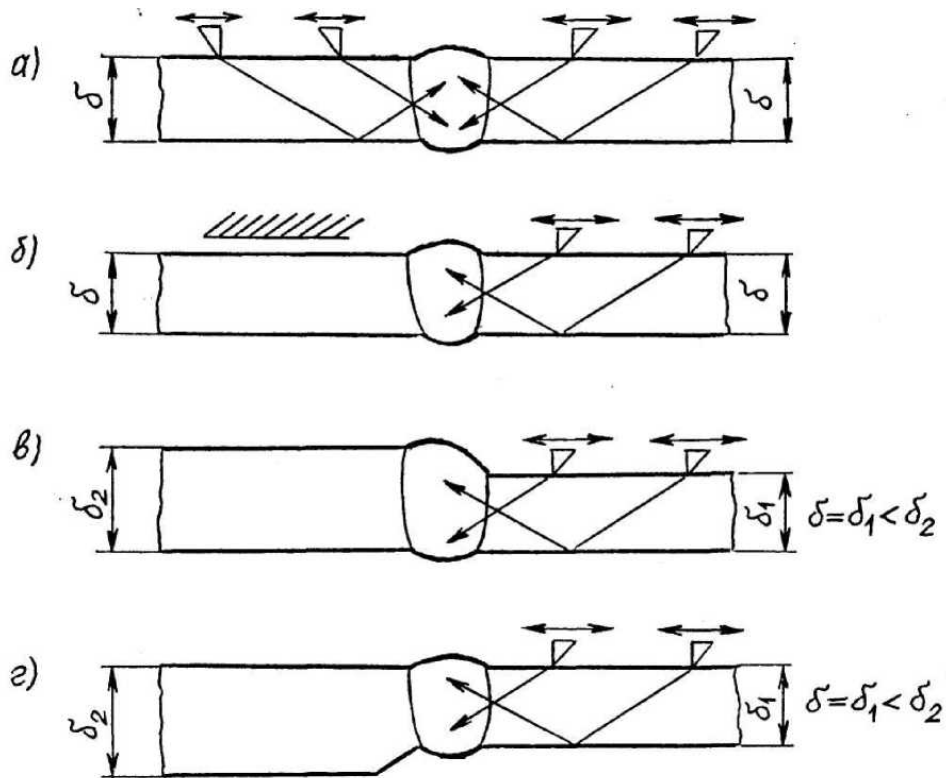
Схема проведення ультразвукового контролю: а) – з двох сторін зварного шва в одній площині; б) – з однієї сторони зварного шва; в), г) – різнотовщинних деталей
